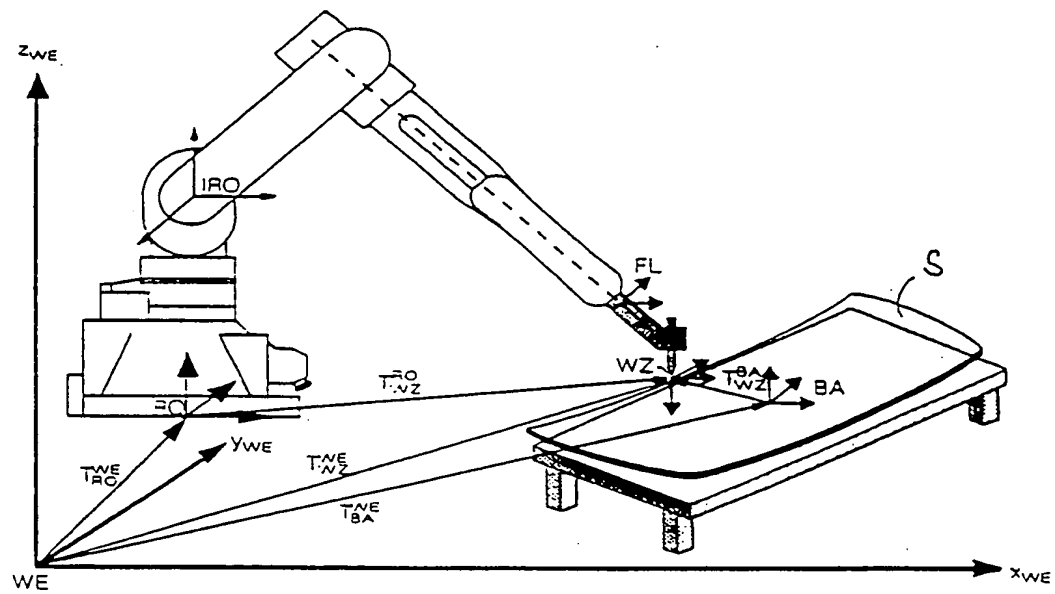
Führung des Werkzeugs über ein ortsfestes Werkstück
